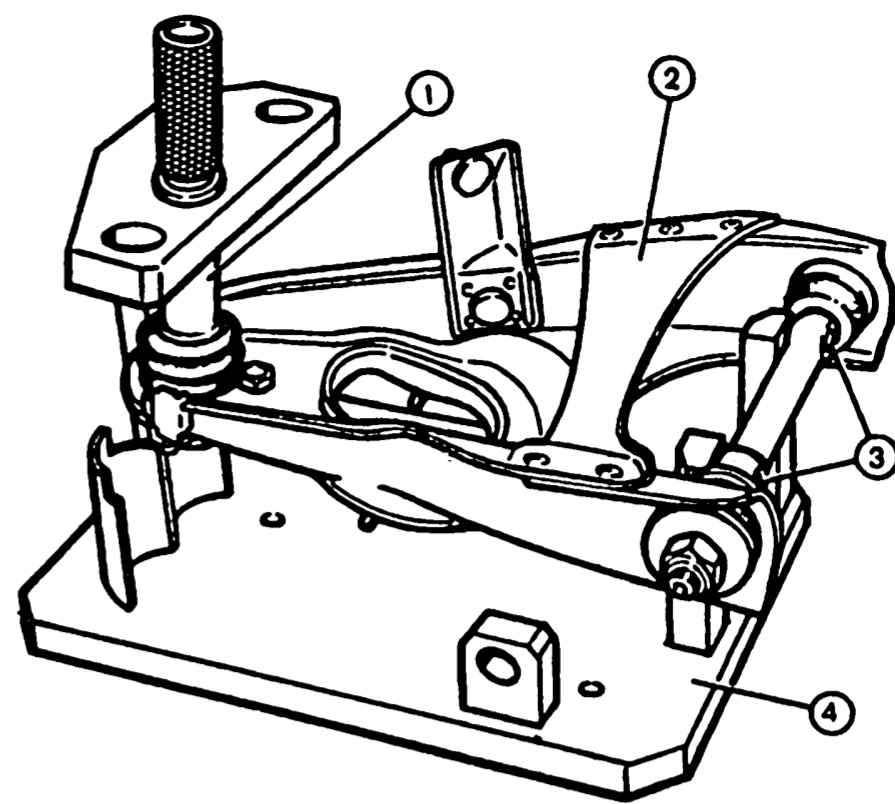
Проверка левого нижнего рычага: 1 - оправка для центровки шарового шарнира; 2 - нижний рычаг; 3 - отверстие для установочных пальцев приспособления А.95716; 4 - приспособление А.95716 для проверки рычагов
